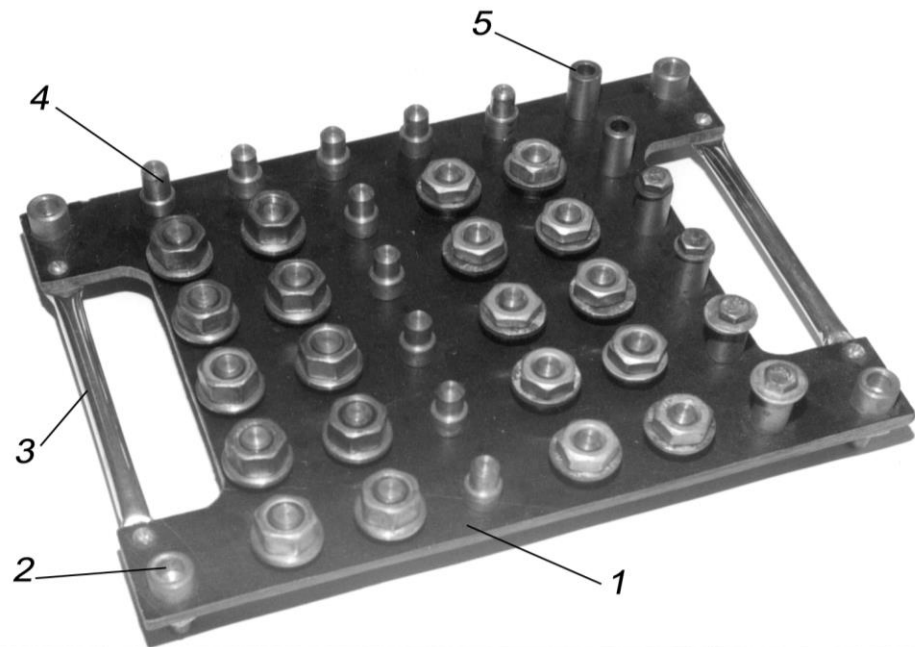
Касета для кріпильних виробів: 1 – плита; 2- ніжки; 3 – ручка; 4- базові штирі для шайб і гайок; 5 – базові гнізда для болтів з шайбами.
